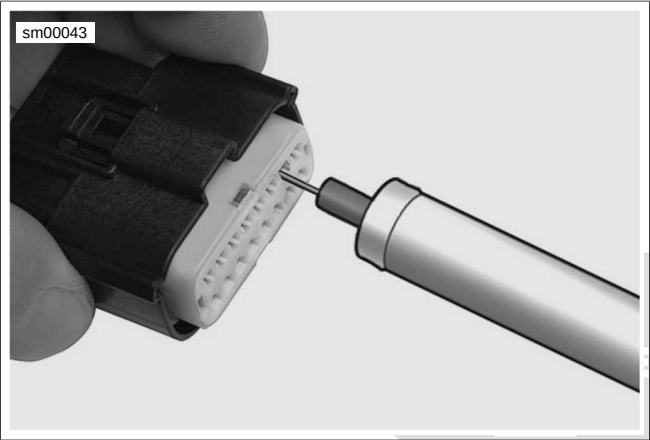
Conector Molex: Extractor de terminales (HD-48114)
